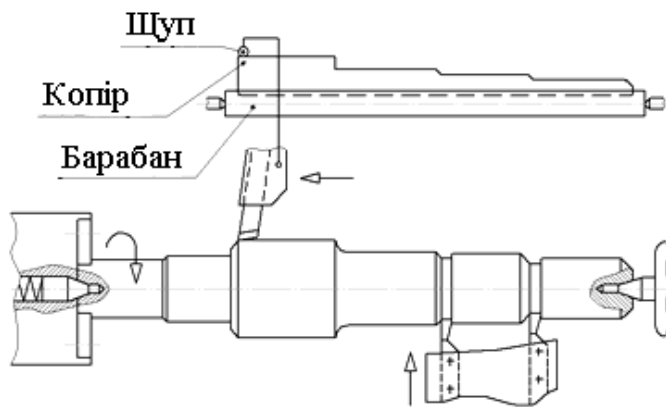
Схема обробки заготовки на токарному гідрокопіювальному напівавтоматі
